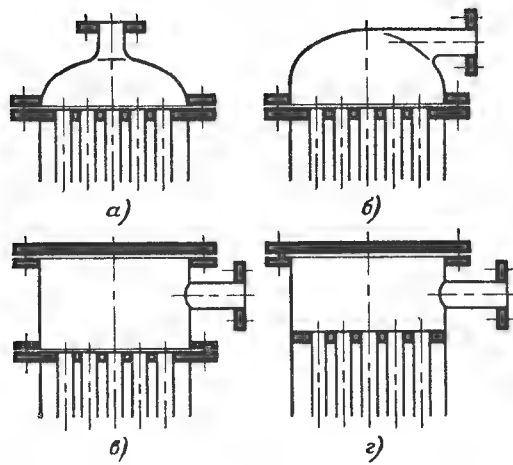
Типы соединений крышки с корпусом аппарата и трубопроводами.
